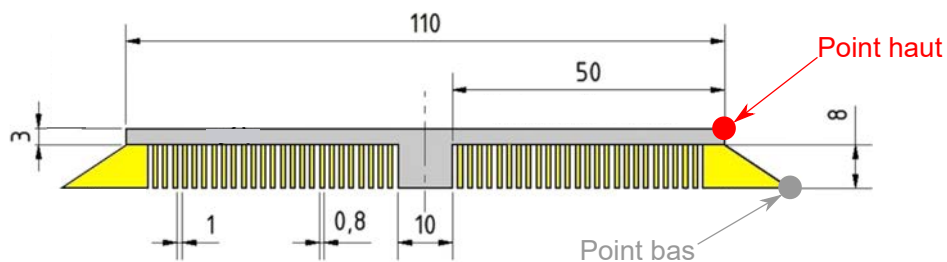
Plan des cantilevers d'après Buchbinder et al. [78]
